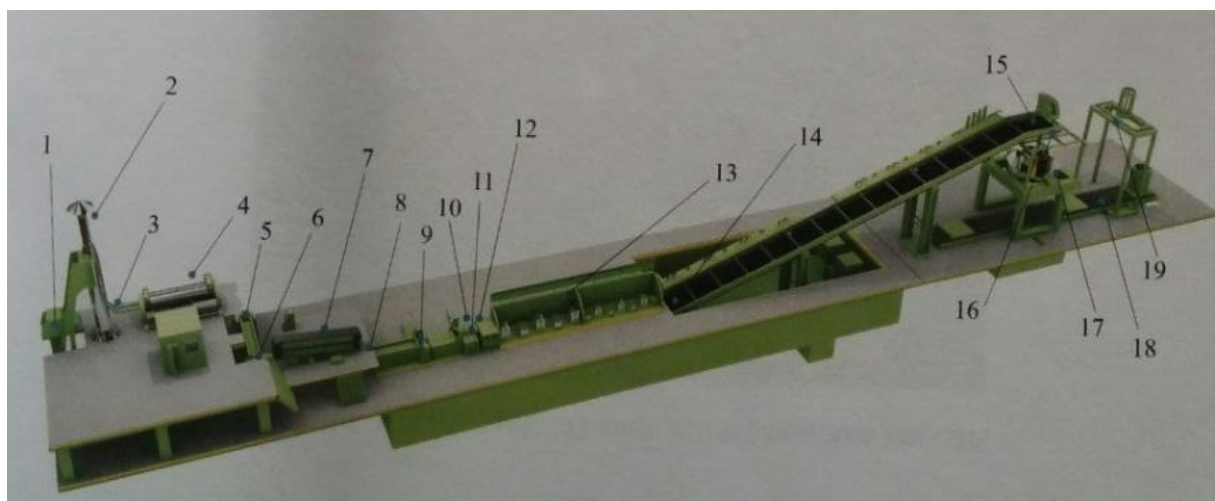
Схема расположения оборудования литейно-прокатного агрегата:
